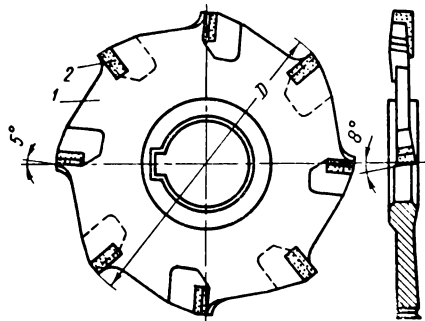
Дисковая трехсторонняя фреза с припаянными пластинками из твердого сплава:
